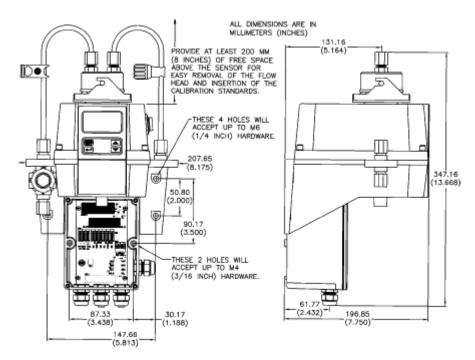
Dimensiones para montaje del 45TURB-1000EP
